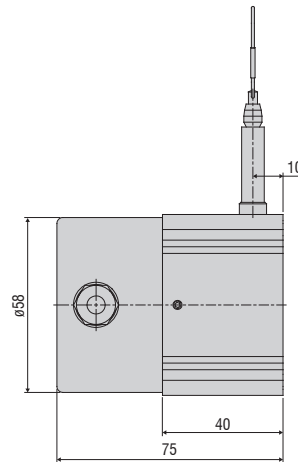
Maßzeichnung WDS- ... - P60 - CR - HTL/TTL
